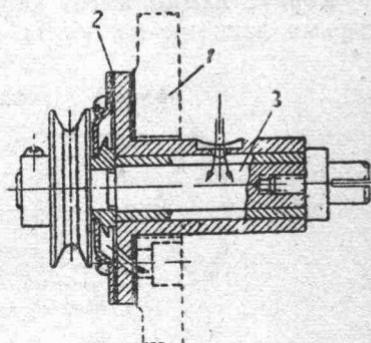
Приводной валик: 1 — средняя крышка; 2 — подшипник; 3 — приводной валик
